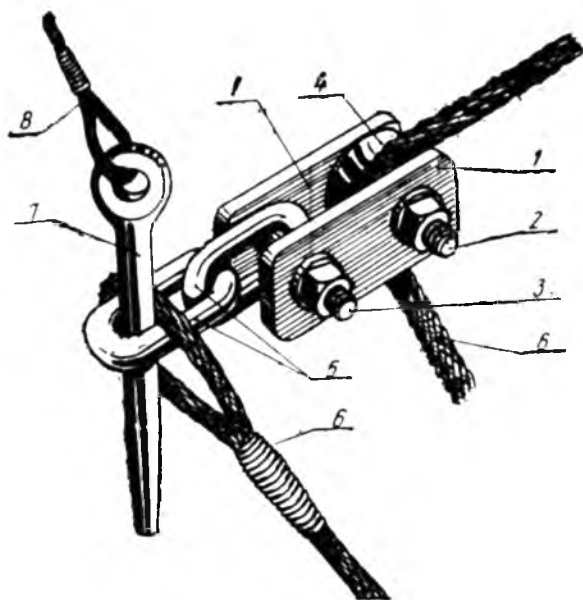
Приспособление с роликом, цепными звеньями и штырем для саморасцепки пачек бревен при работе лебедками: 1 — щеки; 2 — ось ролика; 3 — ось цепных звеньев; 4 — ролик; 5 — цепные звенья; 6 — рабочий строп; 7 — штырь; 8 — вспомогательный строп.
